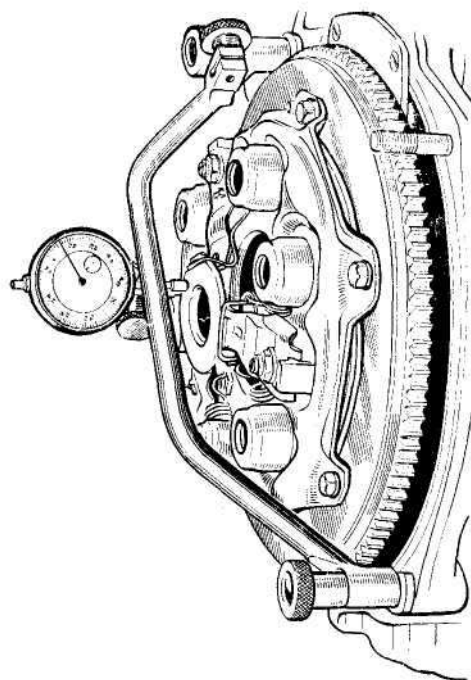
Приспособление для регулировки положения пяты сцепления на двигателе
